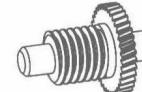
(f) 所示为塑料双联齿轮组件，小齿轮为直齿轮（或小斜齿轮），大齿轮为斜齿轮。在 Valeo 雨刮器和座椅调角器的传动轮系中，这类双联塑料齿轮中的大、小齿轮均为斜齿轮；对双联齿轮的轮齿还有严格的选向方位要求，否则将造成装配上的困难。以上这些要求，采用模塑成型的塑料齿轮都是不难办到的。
